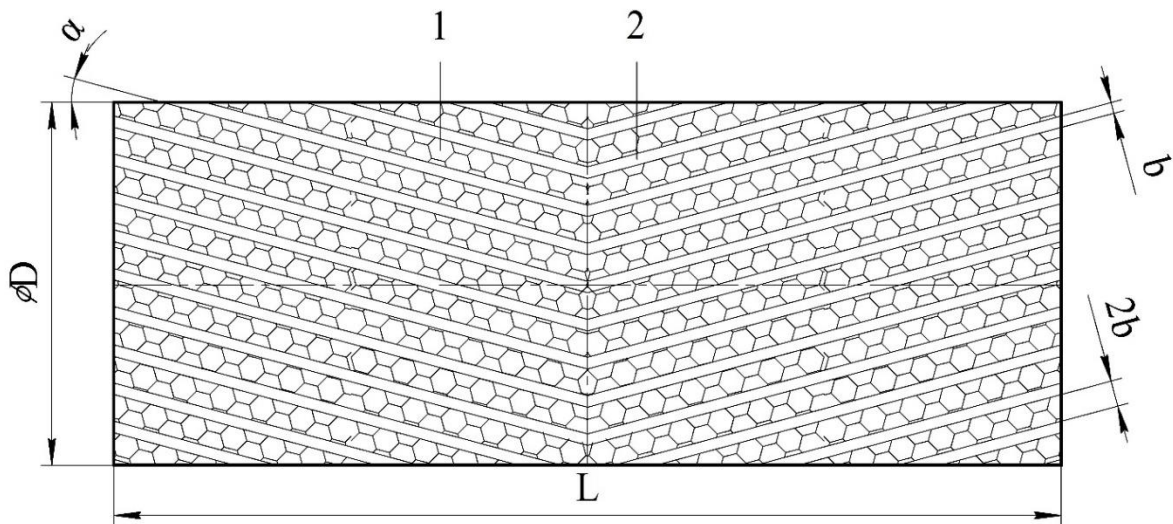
Зміцнювальна обробка циліндричної поверхні притискного валу механізму координатного транспортування, 1 – постійний регулярний мікрорельєф; 2 – частково регулярний мікрорельєф; b – ширина плоскопаралельних заглибин; $2b$ – відстань між заглибинами; α – кут нахилу заглибин; $\varnothing D$ – діаметр роликів; L – ширина роликів.
